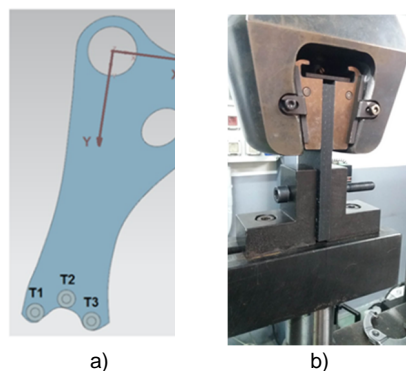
a) Taladros de fijación a rótula, b) Ensayo de bearing.
